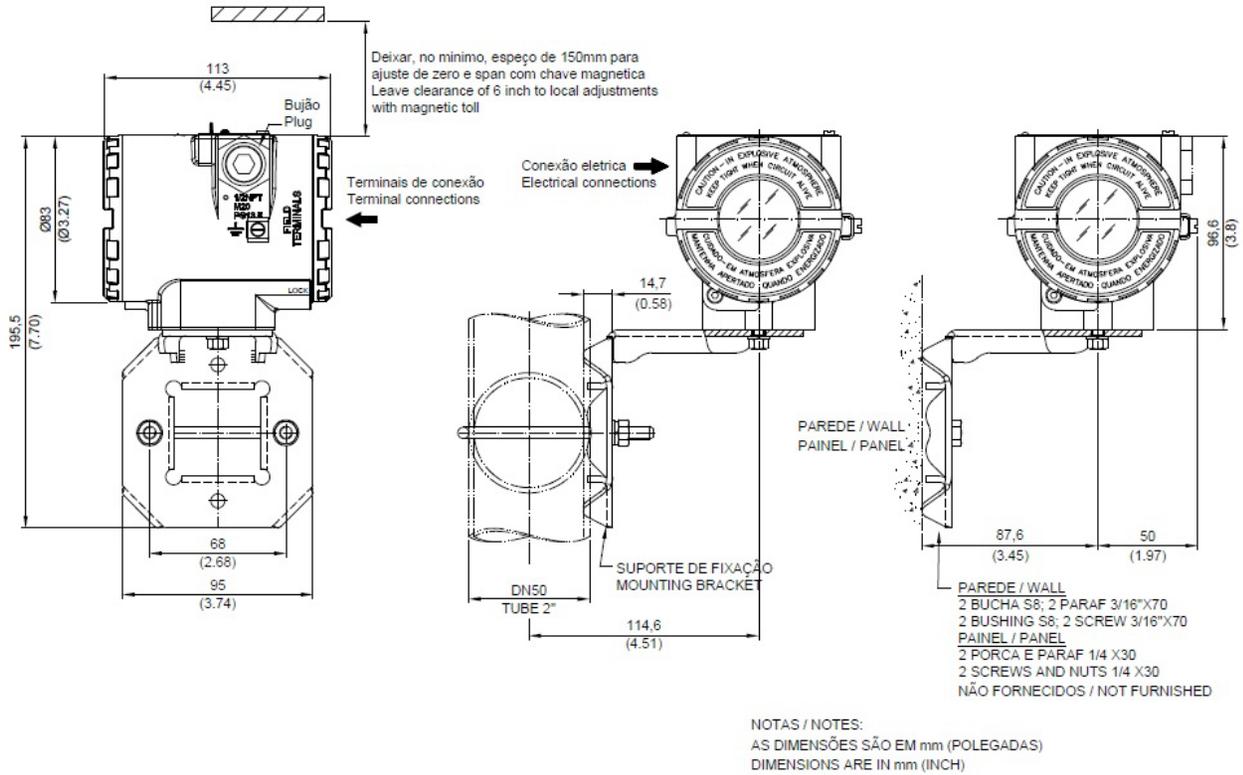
Posições de Montagem e Desenho Dimensional
